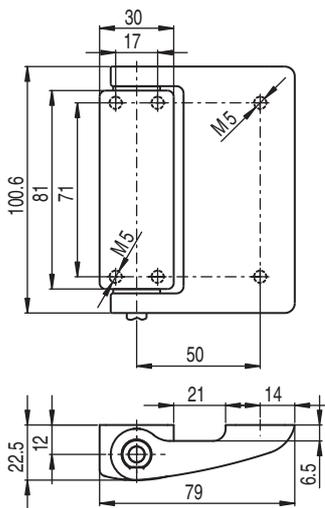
Dimensioni S410-M1CB2-B in mm
